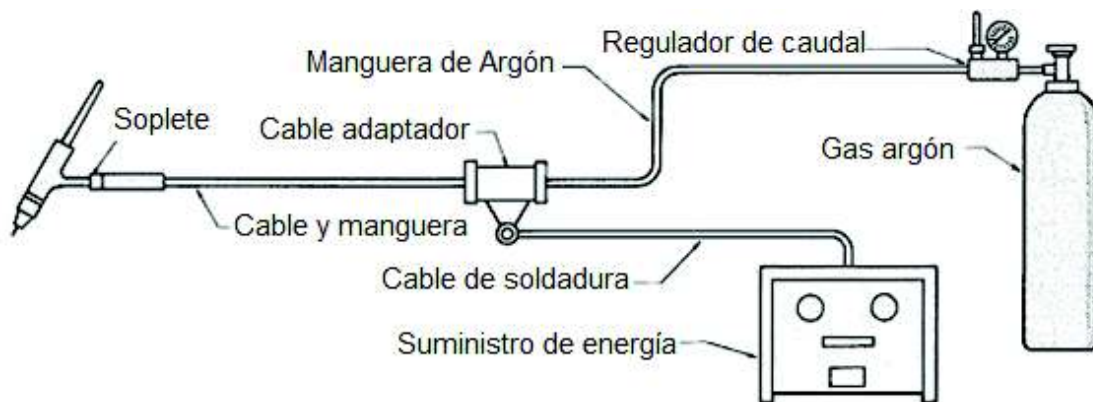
Esquema del sistema de soldadura GTAW (TIG).
